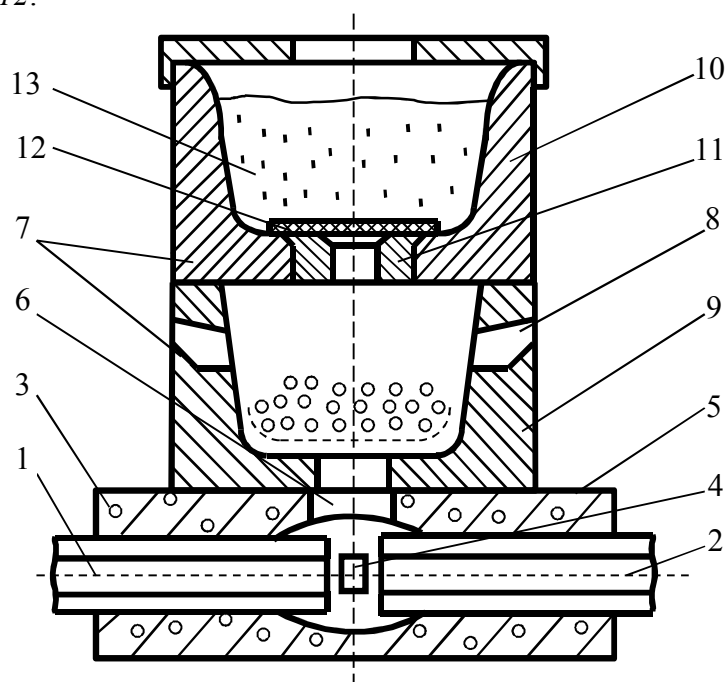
Конструкція металотермічного реактора для зварювання: 1, 2 – чавунні плити з СЧ20 товщиною 30 мм, 3 – формувальна суміш, 4 – пінополіуретанова вставка у порожнині зварювання, 5 – опока, 6 – вертикальний ливарний канал, 7 – двокамерний реактор, 8 – отвір, 9 – нижня камера, 10 – верхня камера, 11 – стержень з отвором, 12 – пластинка, 13 – суміш терміту та графітового порошку
